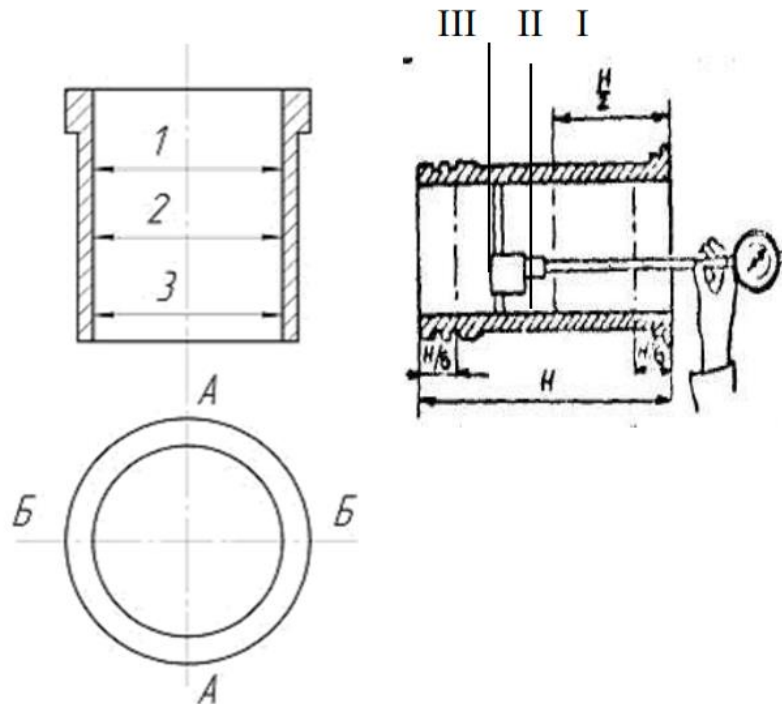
Схема вимірювання діаметра гільзи циліндра
